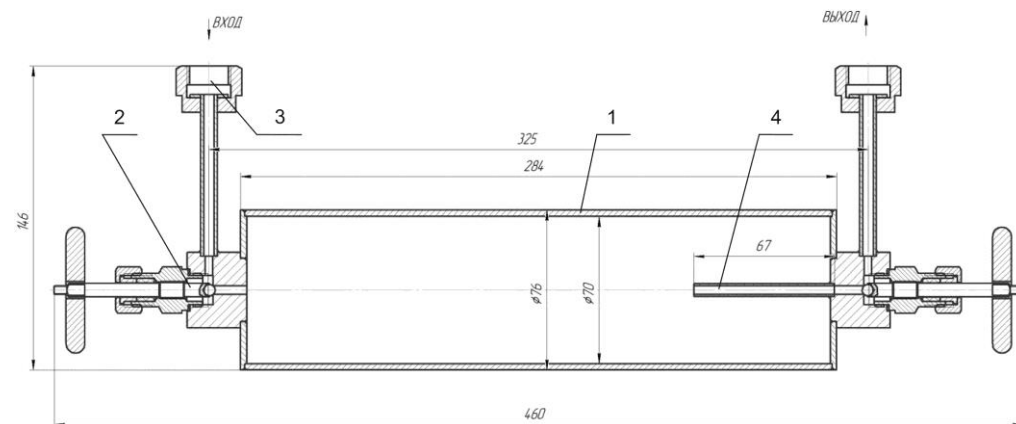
Пробоотборник для аммиака: 1-Корпус, 2-Вентиль, 3-Присоединительный штуцер, 4-Сливная трубка.
